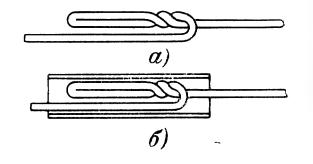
Сварка торцовой поверхности скрутки.
